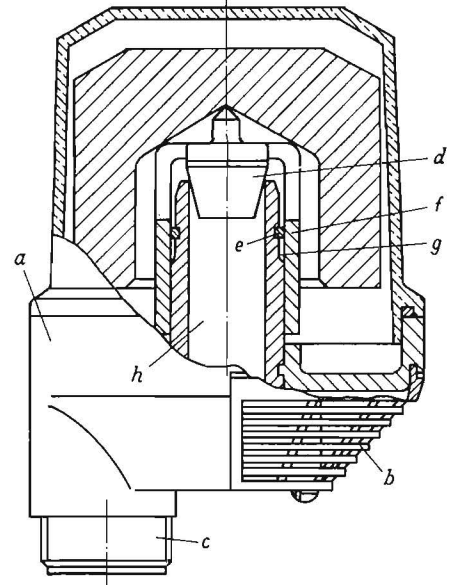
Vakuumentil in einer zum Teil als Schnitt gezeichneten Seitenansicht
